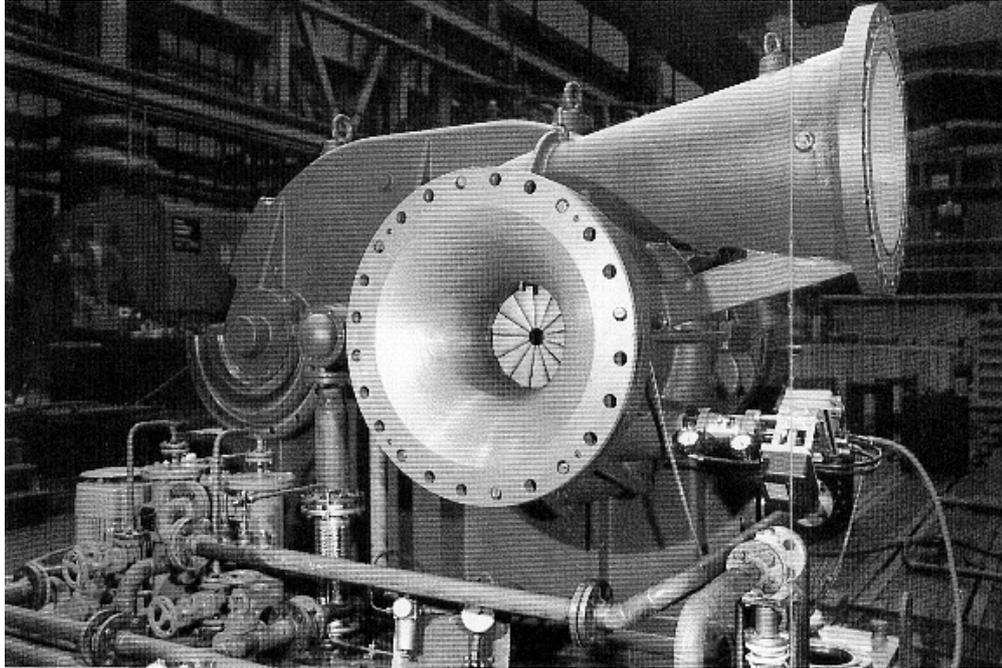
б. Конструкция одноступенчатого центробежного нагнетателя, совмещенного с повышающей зубчатой передачей и регулируемым входным направляющим аппаратом
